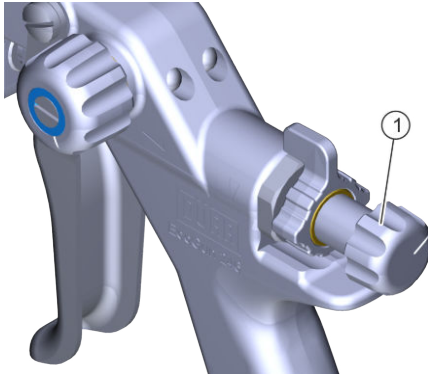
Gesamtluftdruck und Materialmenge einstellen
